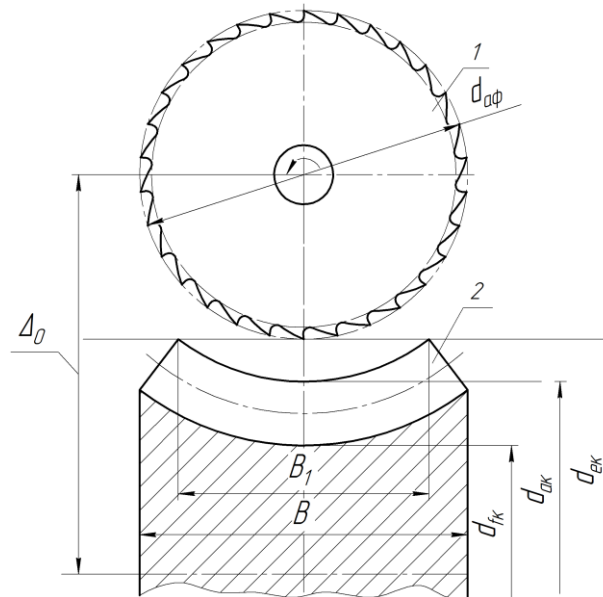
Початкове положення дискової фрези 1 ($z=30$; $m=1,6$; $b=2$;) відносно оброблюваного глобоїдного червячного колеса 2.
